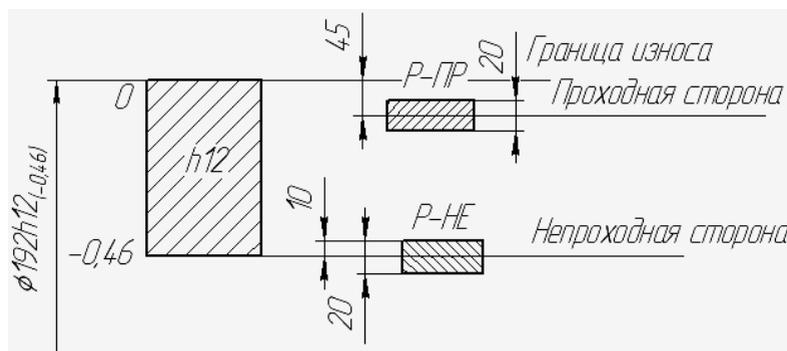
Схема полей допусков детали и гладких калибров для вала $\varnothing 192h12$.
